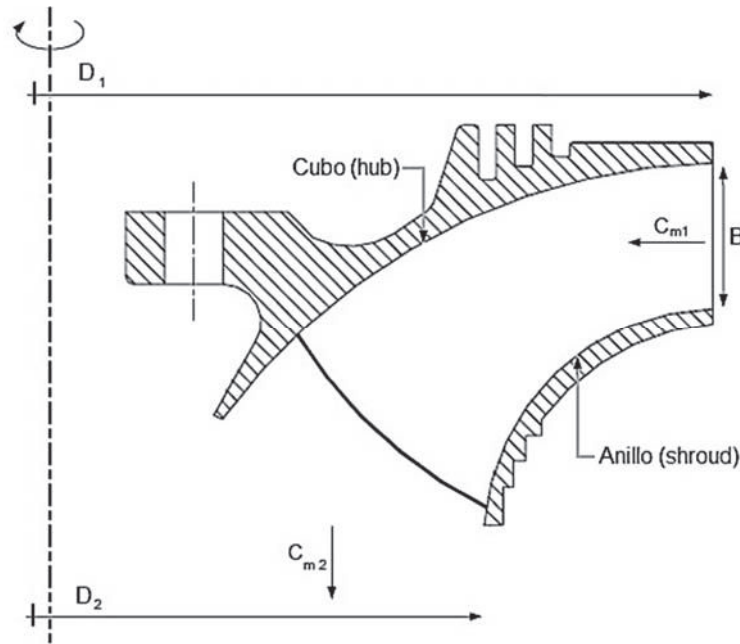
Vista axial del rodete con sus dimensiones principales.
